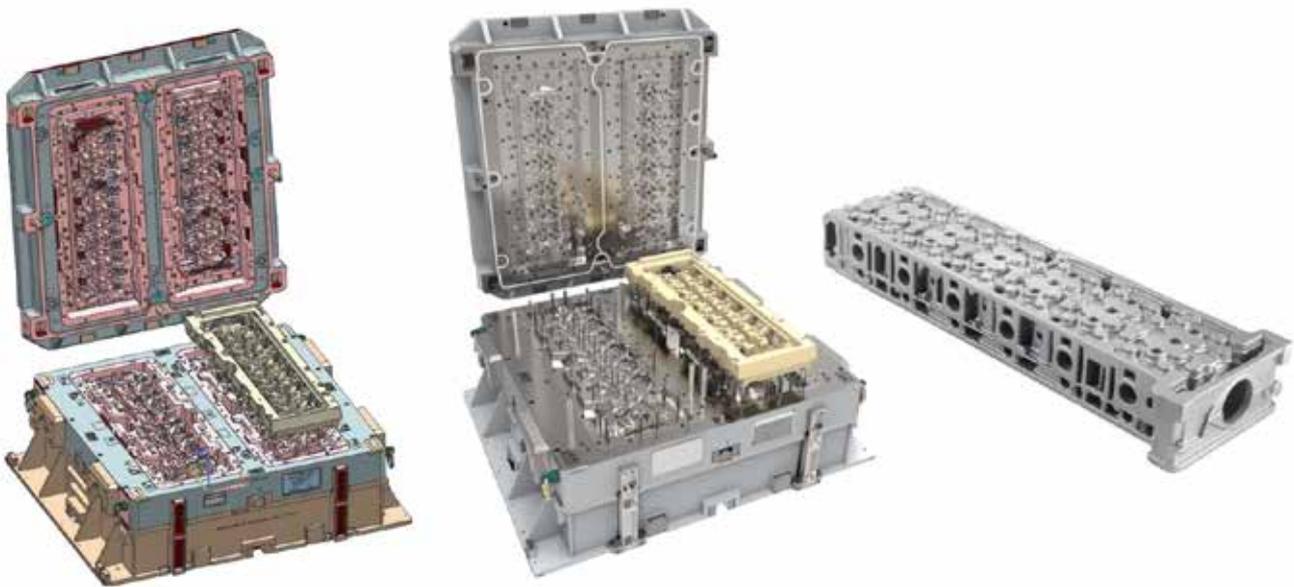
Zylinderkopf. CAD Geometrie, reales Werkzeug, Gussteil – Quelle: DaimlerTruck AG.
